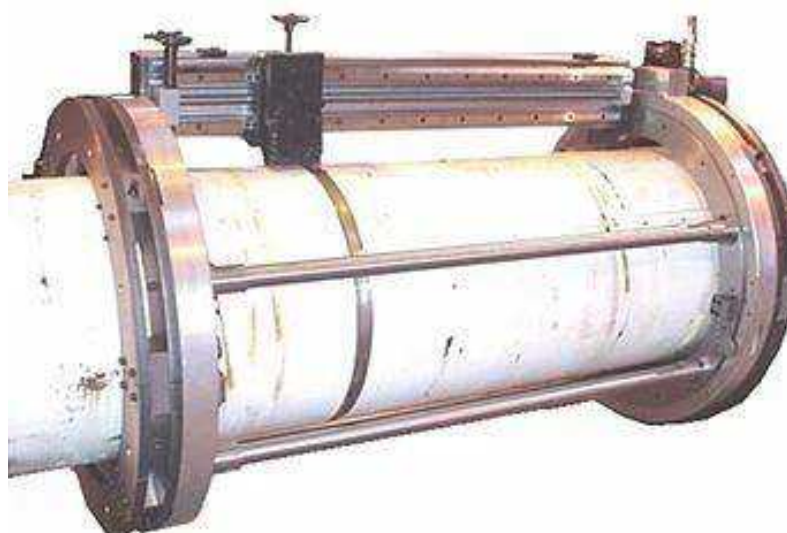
Мобильный токарный станок Mirage Machines MST600
